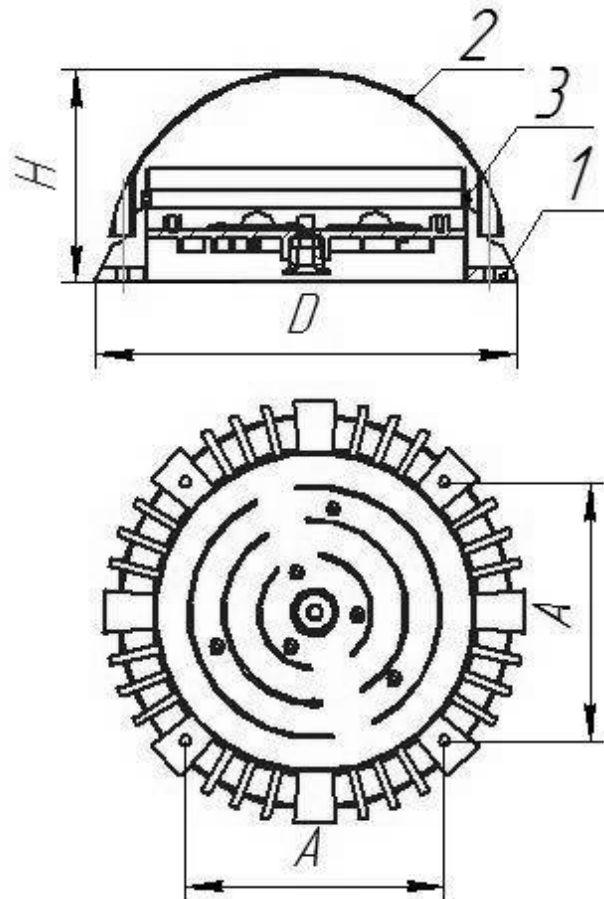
Общий вид, габаритные и присоединительные размеры светильника ДБО84.
